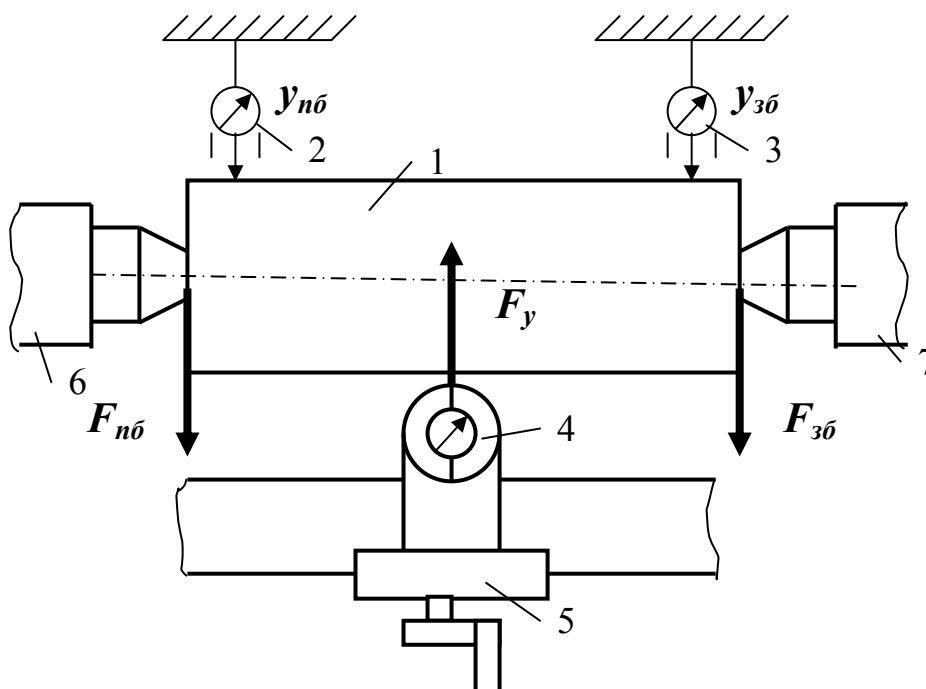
Схема лабораторной установки: 1- обрабатываемая деталь; 2, 3 - индикаторы часового типа; 4- динамометр; 5- суппорт; 6, 7- передняя и задняя бабки станка; $F'_{нб}$ и $F'_{зб}$ – реакции опор на силу F_y .
